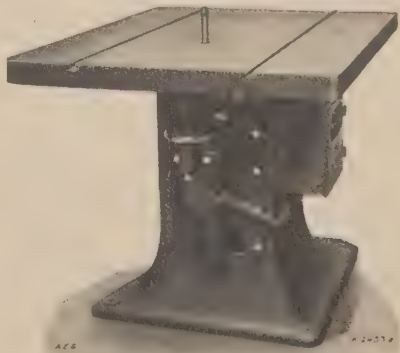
Vollkommener Einbau eines Motors in eine Werkzeugmaschine.
